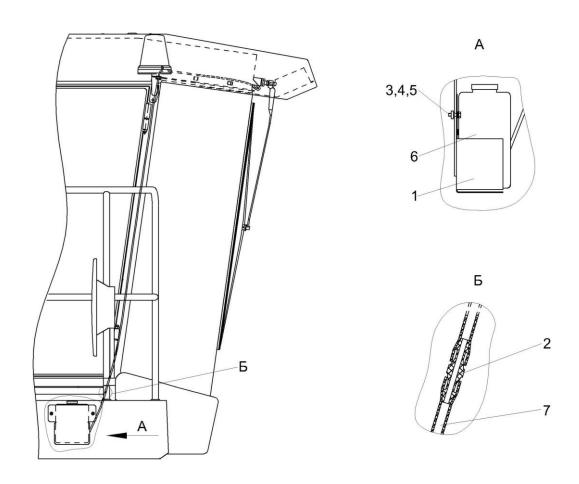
Установка стеклоомывателя КЗК-12-0120460-01
